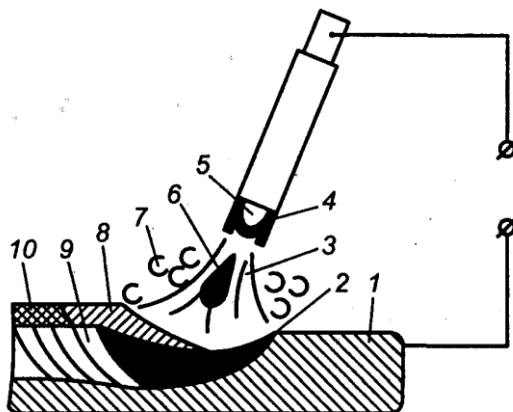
Схема ручной дуговой сварки покрытыми электродами
